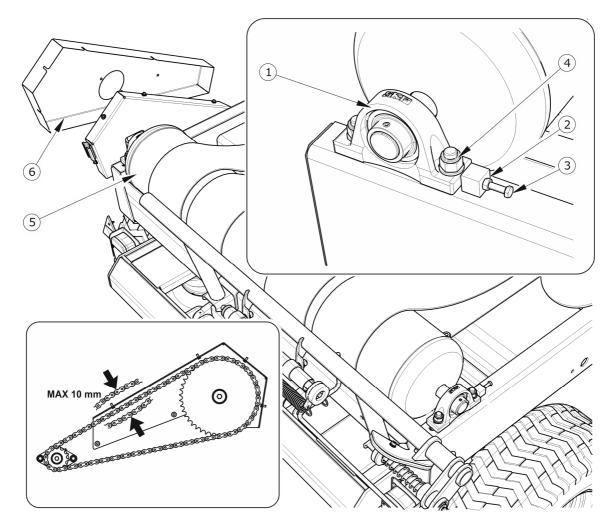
Ajuste y comprobación de la tensión de la cadena de transmisión de rodillos (1) unidad de rodamiento, (2) contratuerca, (3) tornillo de ajuste, (4) tuerca de fijación de la unidad de rodamiento, (5) rodillo de la mesa, (6) tapa del engranaje
